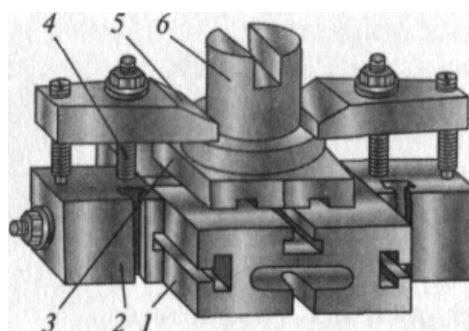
Стандартизоване пристосування на базі прихватів з ручним приводом: 1 – базова плита; 2 – опора; 3 – установна планка; 4 – кріпильний болт; 5 – прихват; 6 – заготовка
